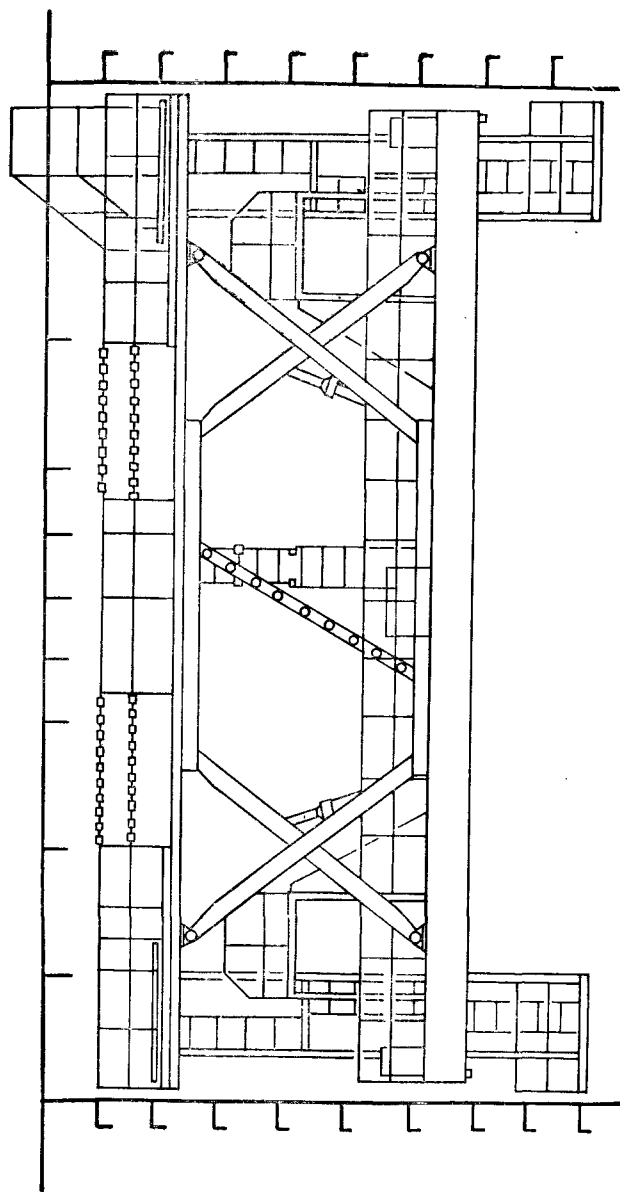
Схема механизированной передвижной платформы для проведения сварочных работ в центральных танках.
